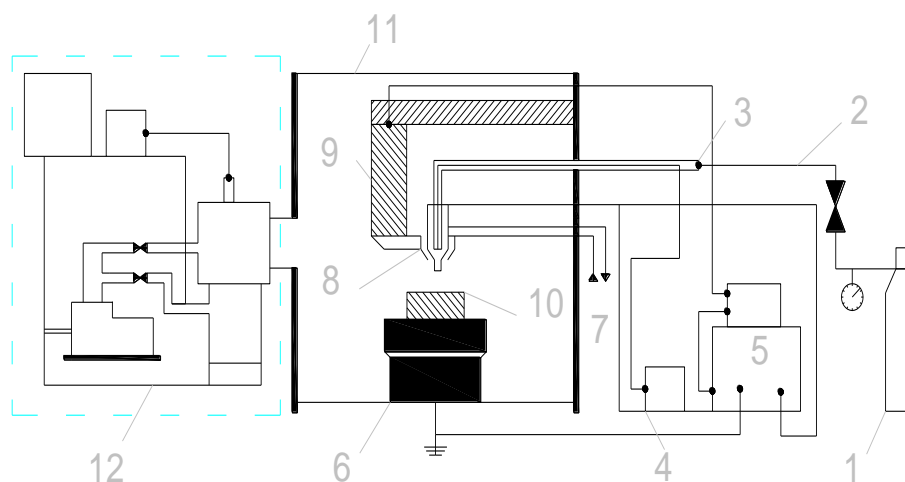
Принципиальная схема установки для сварки горячим полым катодом в вакууме
